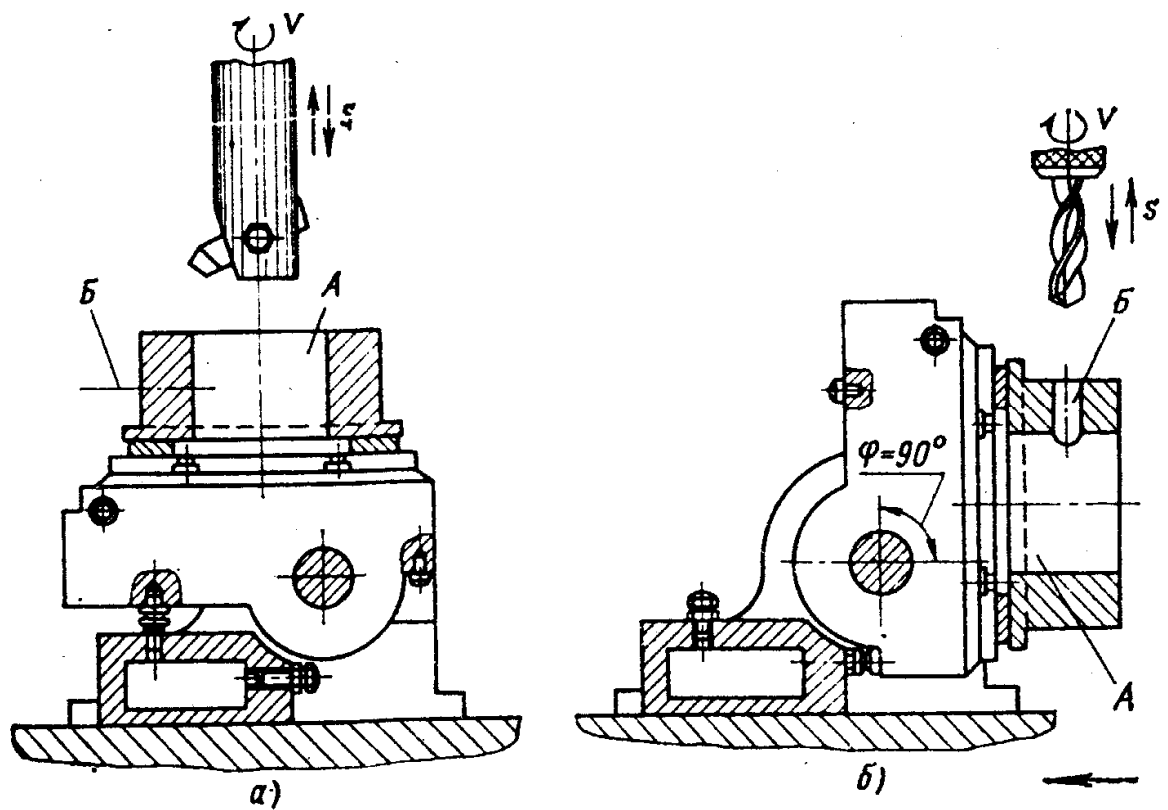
Схема обработки отверстий в матрице пресс-формы на координатно-расточном станке
